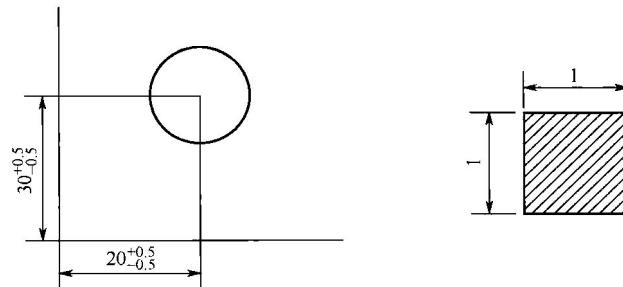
尺寸公差标注和该尺寸公差控制的公差带
